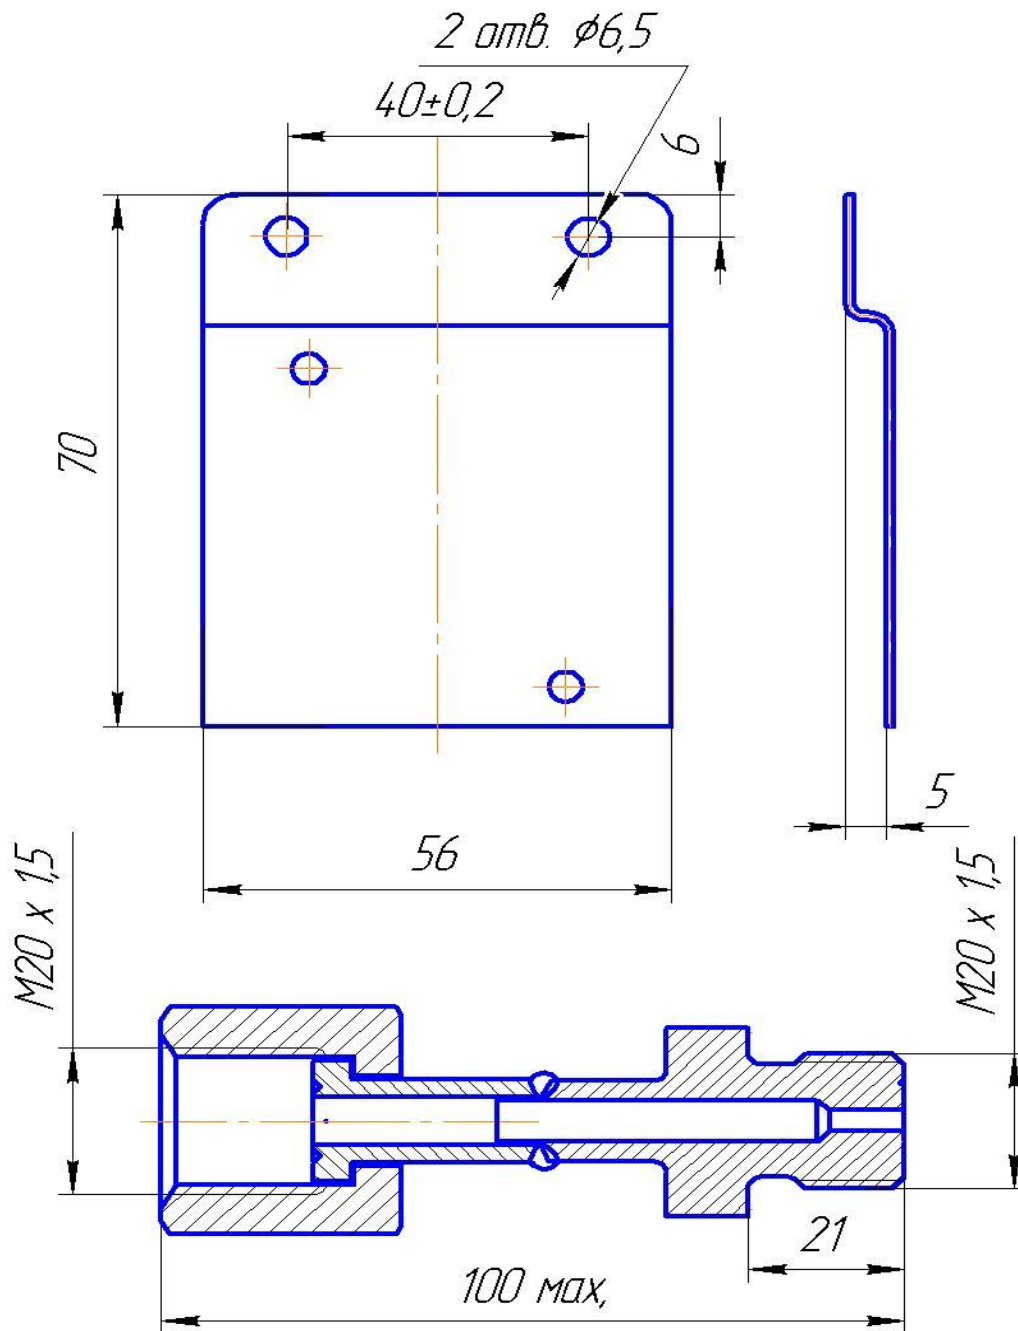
Держатель и КМЧ-2 для крепления датчика ДДМ-03-ДИ (ДВ,ДИВ,ДА)-МИ;
